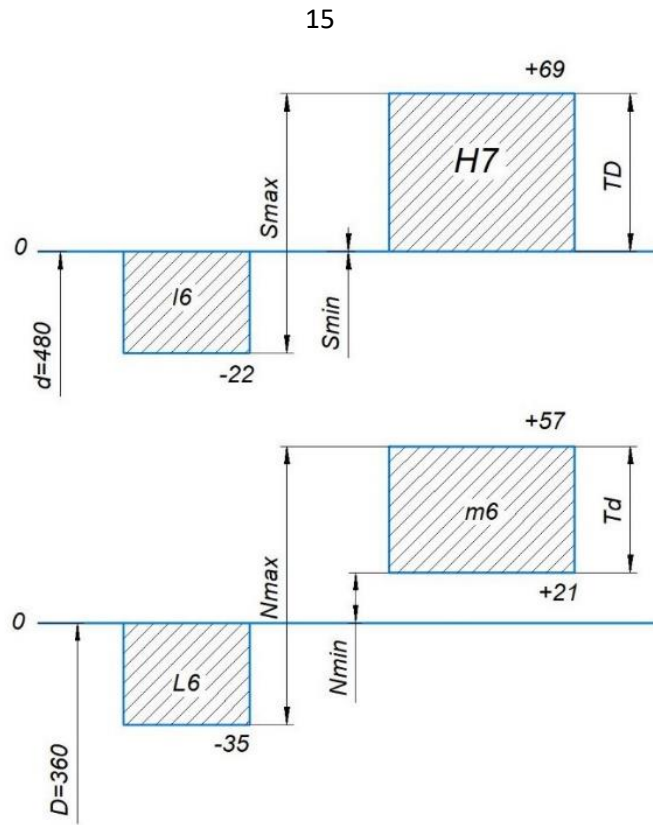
Схема полів допуску підшипника кочення
